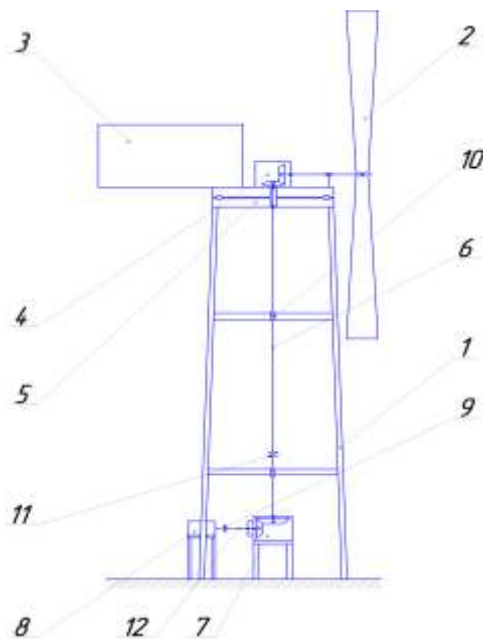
Малогабаритна вітрова установка для виробництва електроенергії – Рама; 2 – вітряк; 3 – направляюча; 4 – верхній конічний редуктор; 5 – поворотний механізм; 6 – вал основний; 7 – нижній конічний редуктор; 8 – генератор; 9 – муфта фрикційна; 10 – підшипниковий вузол; 11 – муфта запобіжна; 12 – вал приводу генератора;
